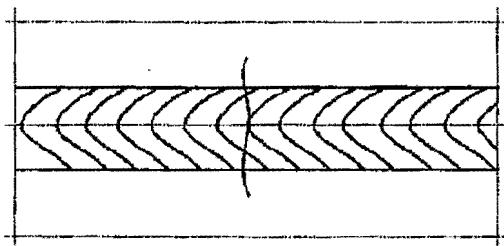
25. Поперечная трещина сварного соединения
